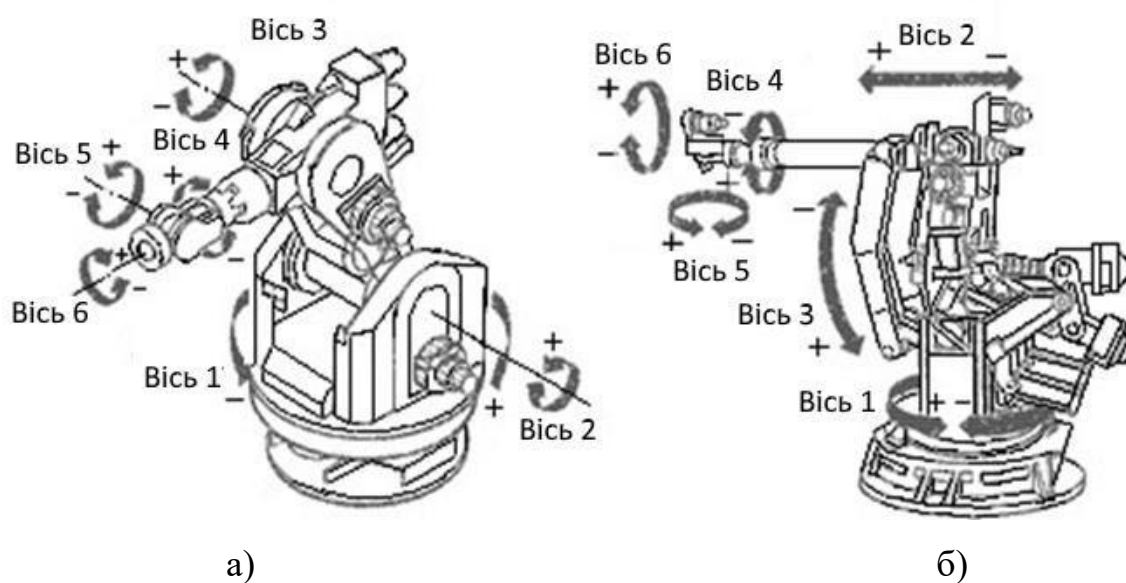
Ступінь рухомості зварювального робота типу IR-160/60 (а) та IR-601/60 (б) німецької фірми "Kuka" [5]
